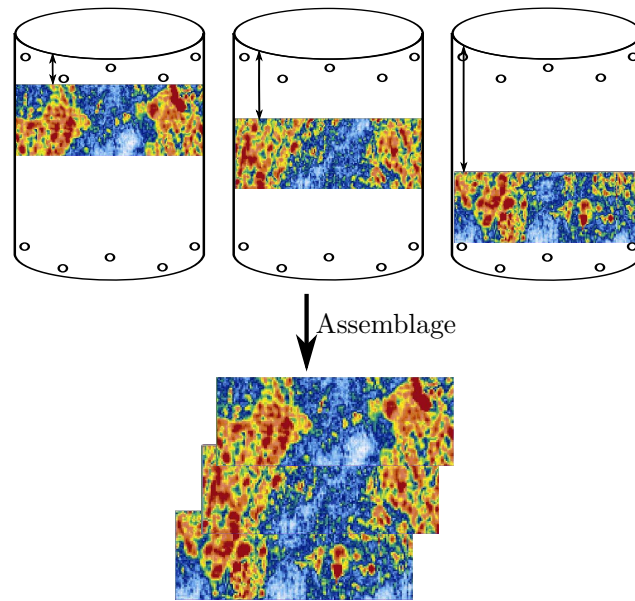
Mesures par ultrasons sur tube : trois C-scans indépendants et leur assemblage
